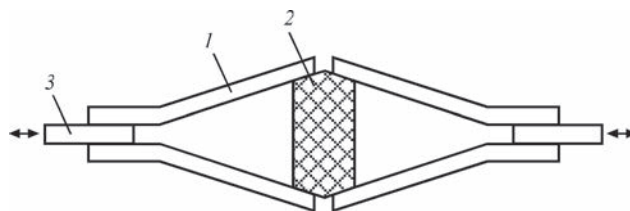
Схема составного образца для малоциклового испытания сварных соединений с угловой деформацией: 1 — испытываемые элементы; 2 — демпфер; 3 — элемент для закрепления в пульсаторе
